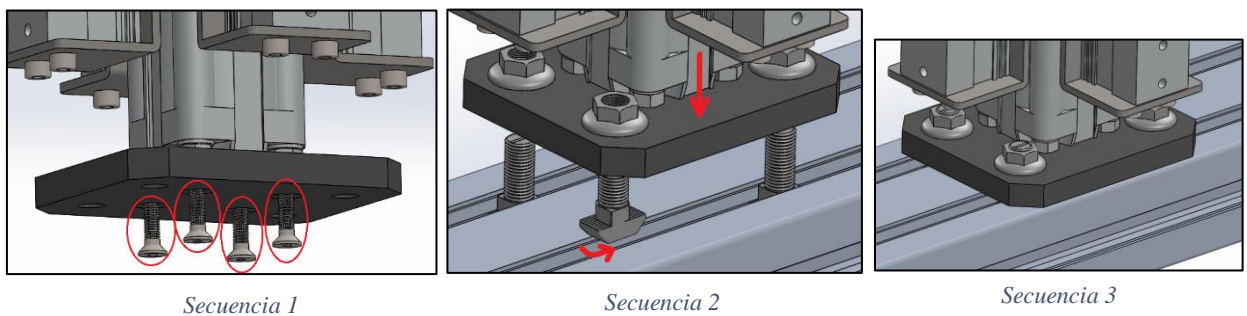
Anclaje subconjunto plataforma base a estructura
